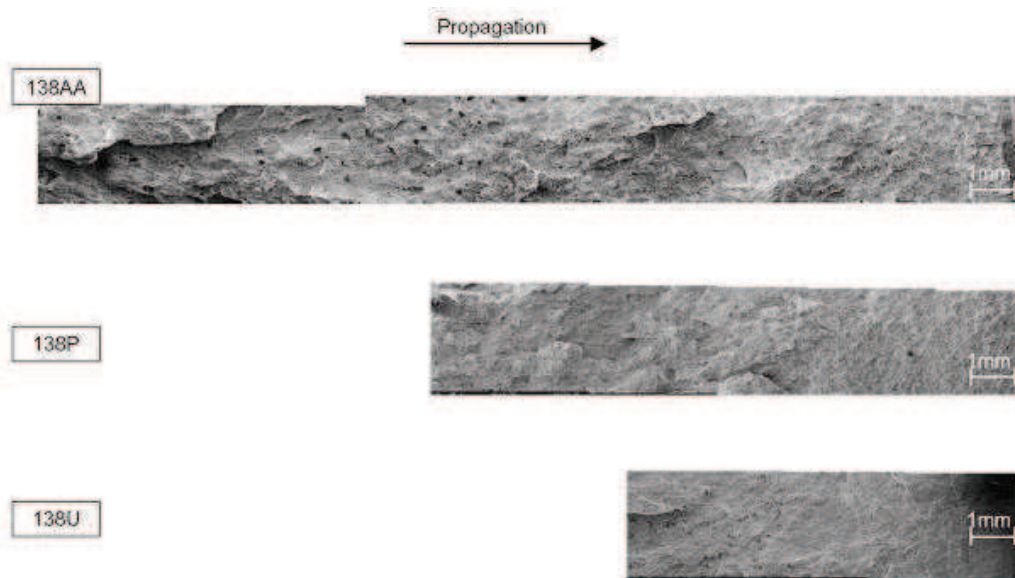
Fractographies des propagations de fissure - éprouvettes CT testées à -100°C
